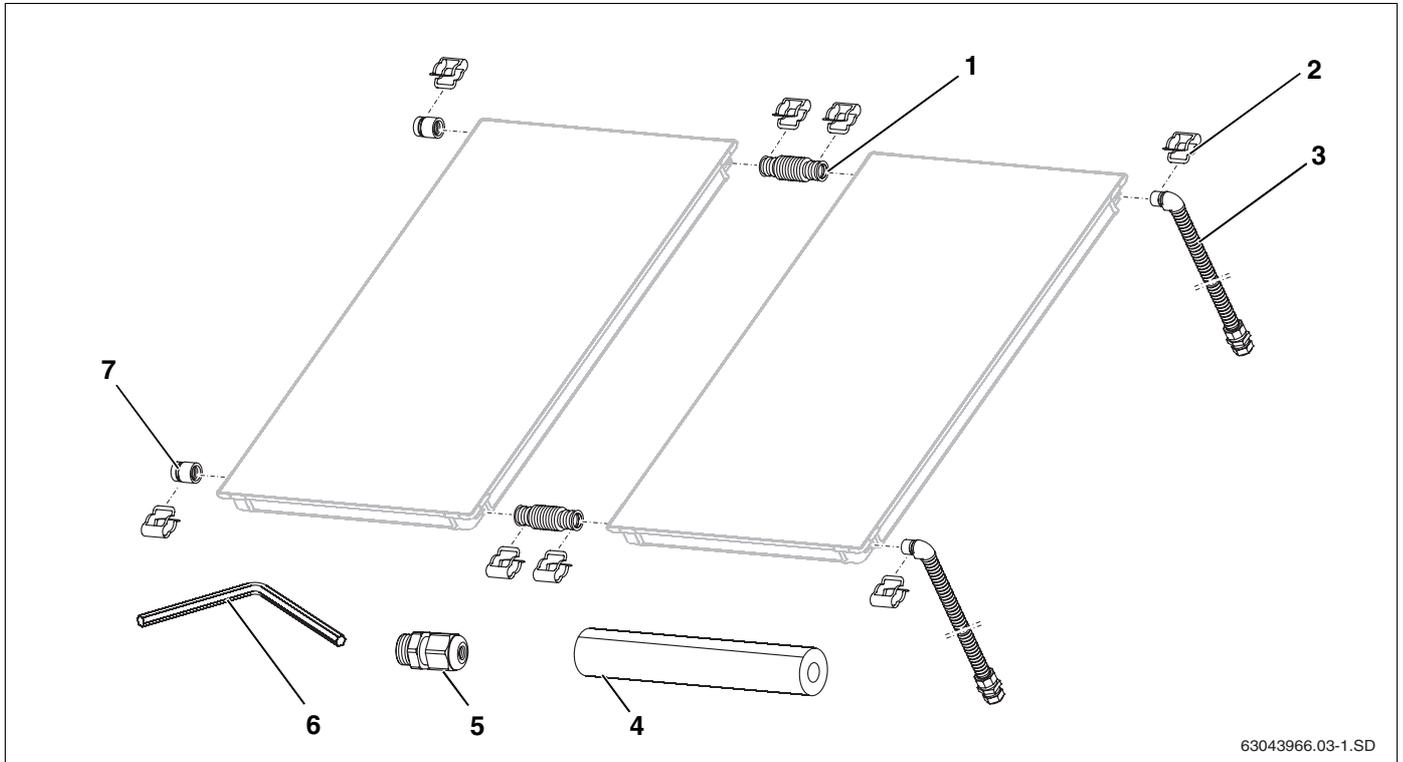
Kit di allacciamento e kit di collegamento (rappresentazione con 2 collettori verticali)
